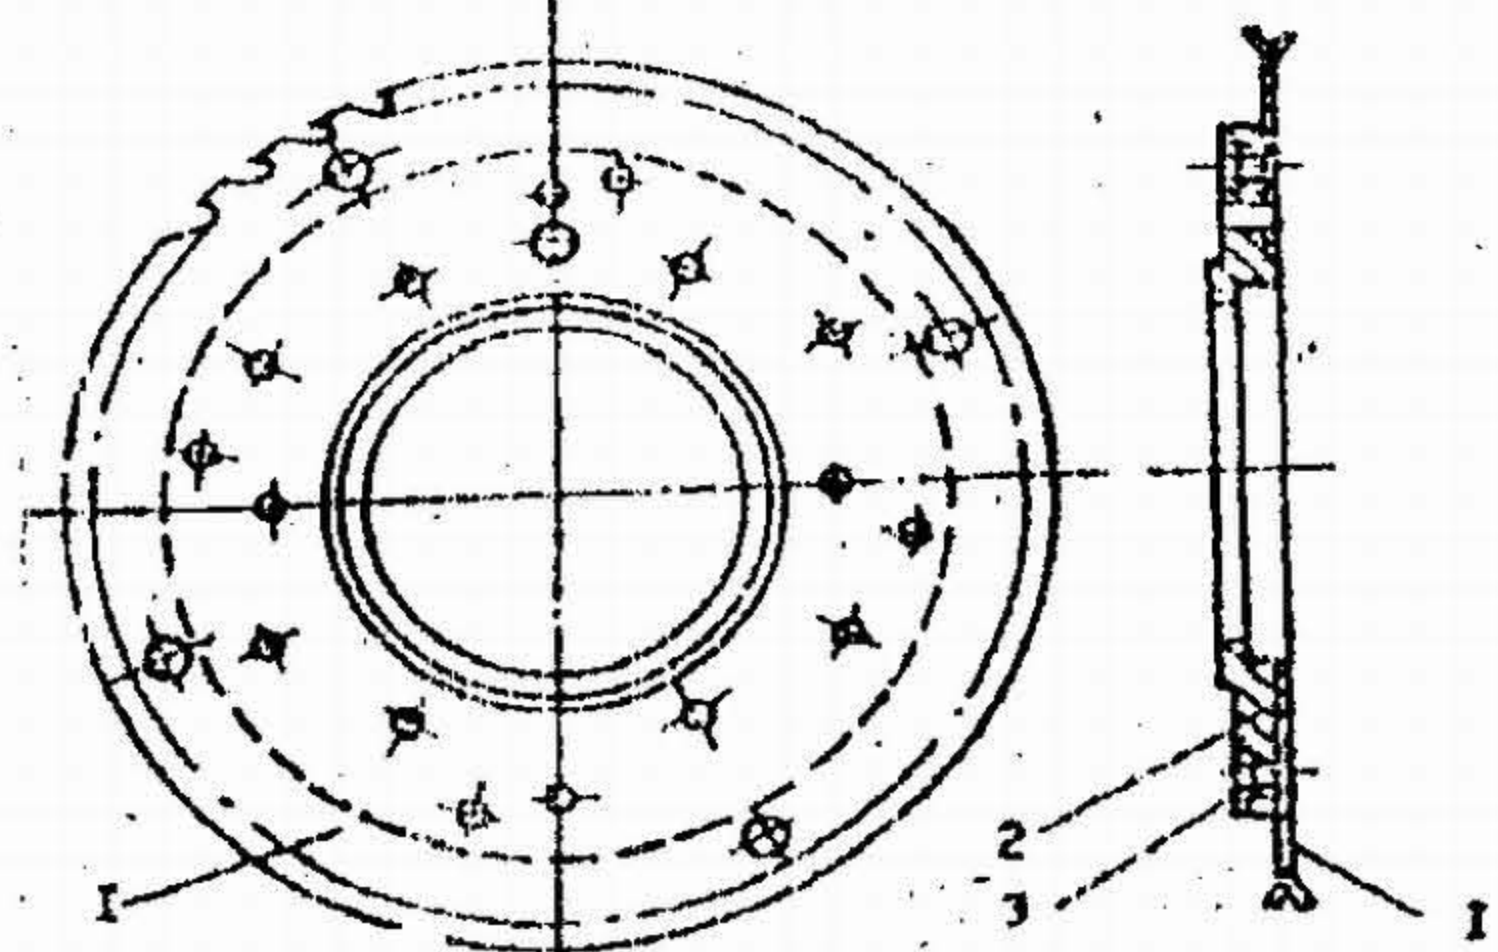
Пила с кольцом: 1-пила; 2-кольцо; 3-защелка
